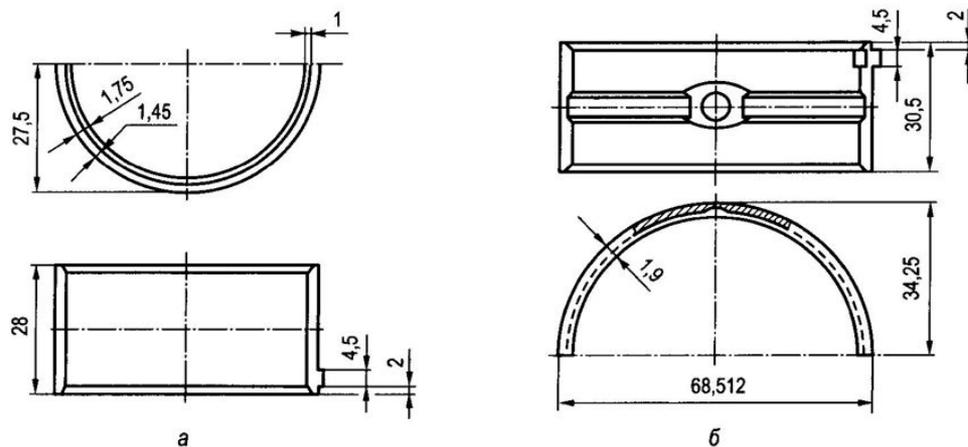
Нижний (а) и верхний (б) вкладыши подшипника
